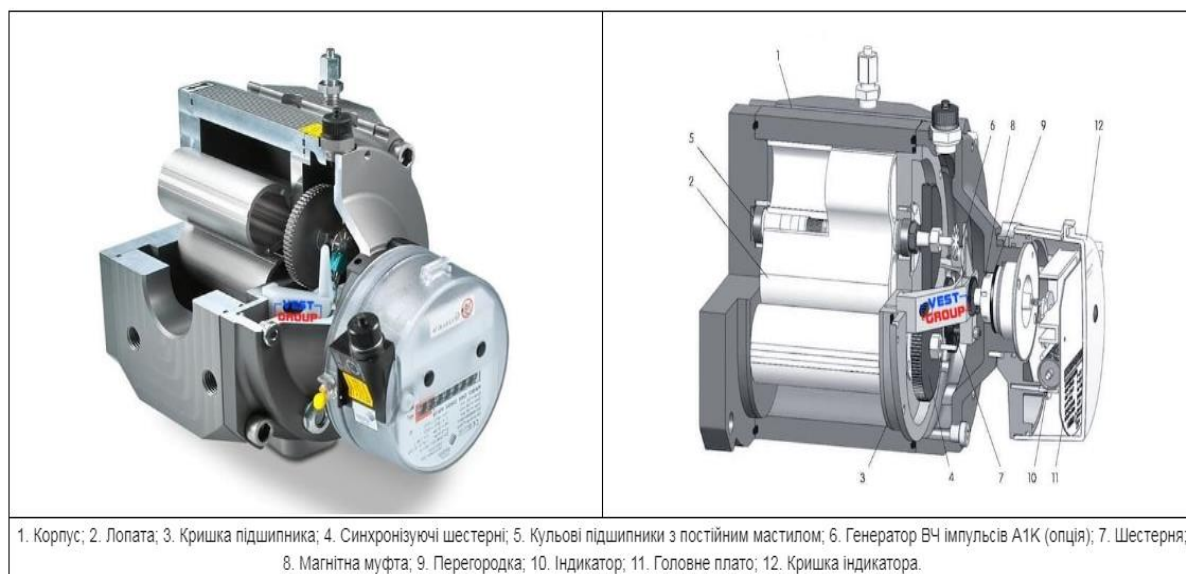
Конструкція еталонного лічильника газу (робочого еталону об'єму газу) роторного типу RABO G65 Dn50 Pn16.
